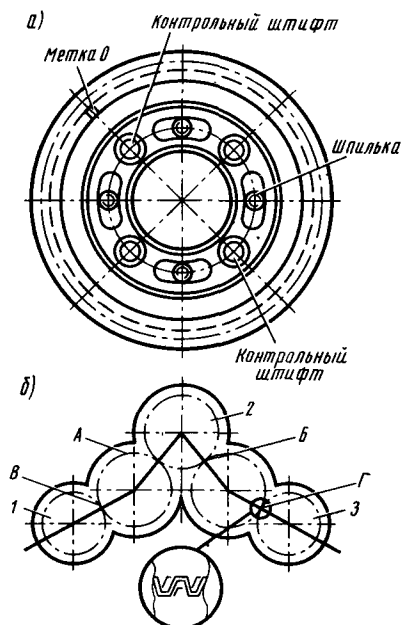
Установка зубчатых колес кулачковых валов топливных насосов дизеля типа Д100:
